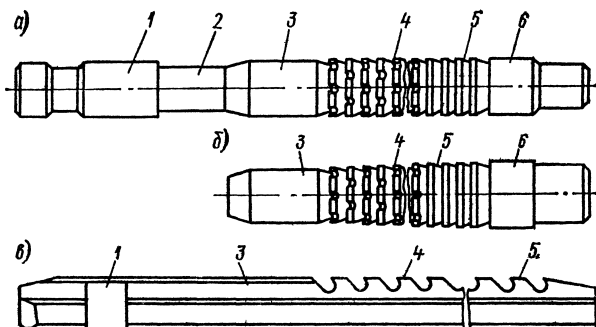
Основные элементы протяжек и прошивок: а — круглая протяжка; б — круглая прошивка; в — шпоночная протяжка;
